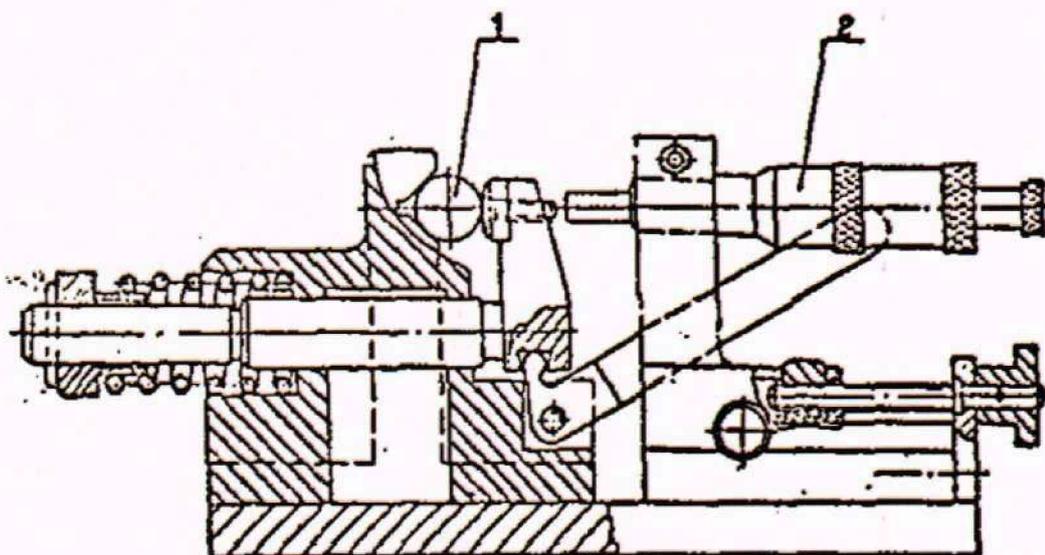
Схема приспособления с микрометрической головкой: 1 – поверяемый нутромер;
